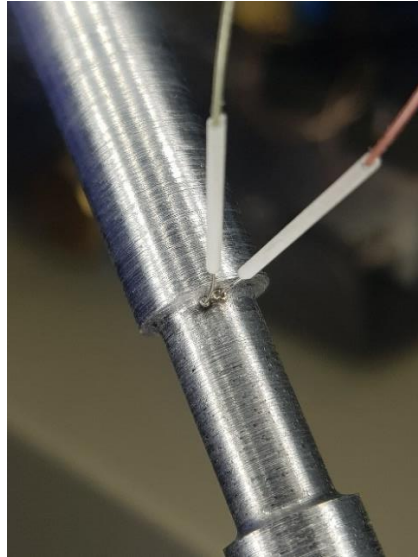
Termopar soldado a probeta de torsión.
